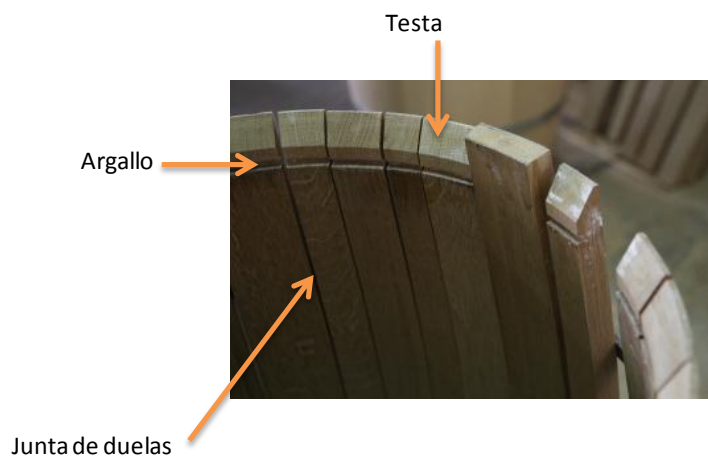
Detalle del extremo de una barrica de roble sin fondar.
